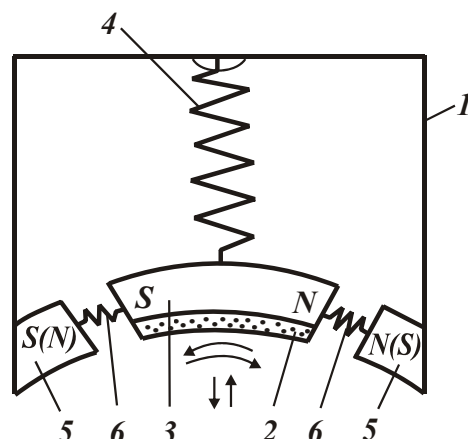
Маятниковая схема электроискрового магнито-импульсного шлифования зубьев, пазов, резьбы, фасок, галтелей вогнутым шлифовальным инструментом: 1 – корпус; 2 – шлифовальный инструмент; 3 – патрон для шлифовального инструмента из магнитных материалов или с электромагнитом; 4 – пружина подвески патрона со шлифовальным инструментом; 5 – управляющие электромагниты; 6 – пружины, отделяющие шлифовальный инструмент от управляющих электромагнитов.
